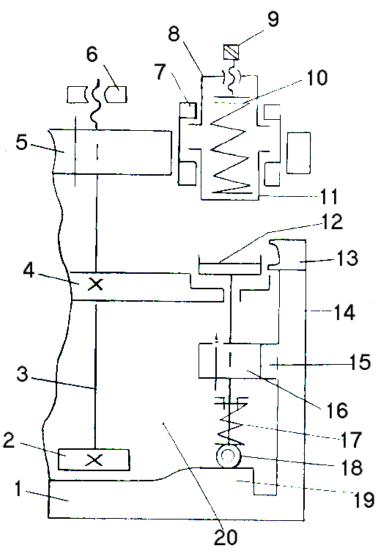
Схема многопозиционного закаточного механизма машины КАН-0-МАТ: 1 — корпус, 2 — шестерня привода карусели, 3 — вал карусели, 4 — карусель, 5 — диск носитель патронов, 6 — гайка для регулировки диска по высоте, 7 — корпус патрона, 8 — стакан, 9 — болт регулировки давления, 10 — пружина прижимная, 11 — тарелка прижимная, 12 — закаточная тарелка, 13 — клинчер — профильный закаточный сегмент, 14 — бурт для установки клинчера, 15 — зубчатый венец, 16 — шестерня привода закаточной тарелки, 17 — возвратная пружина, 18 — толкатель, 19 — копир, 20 — ванна масляная
